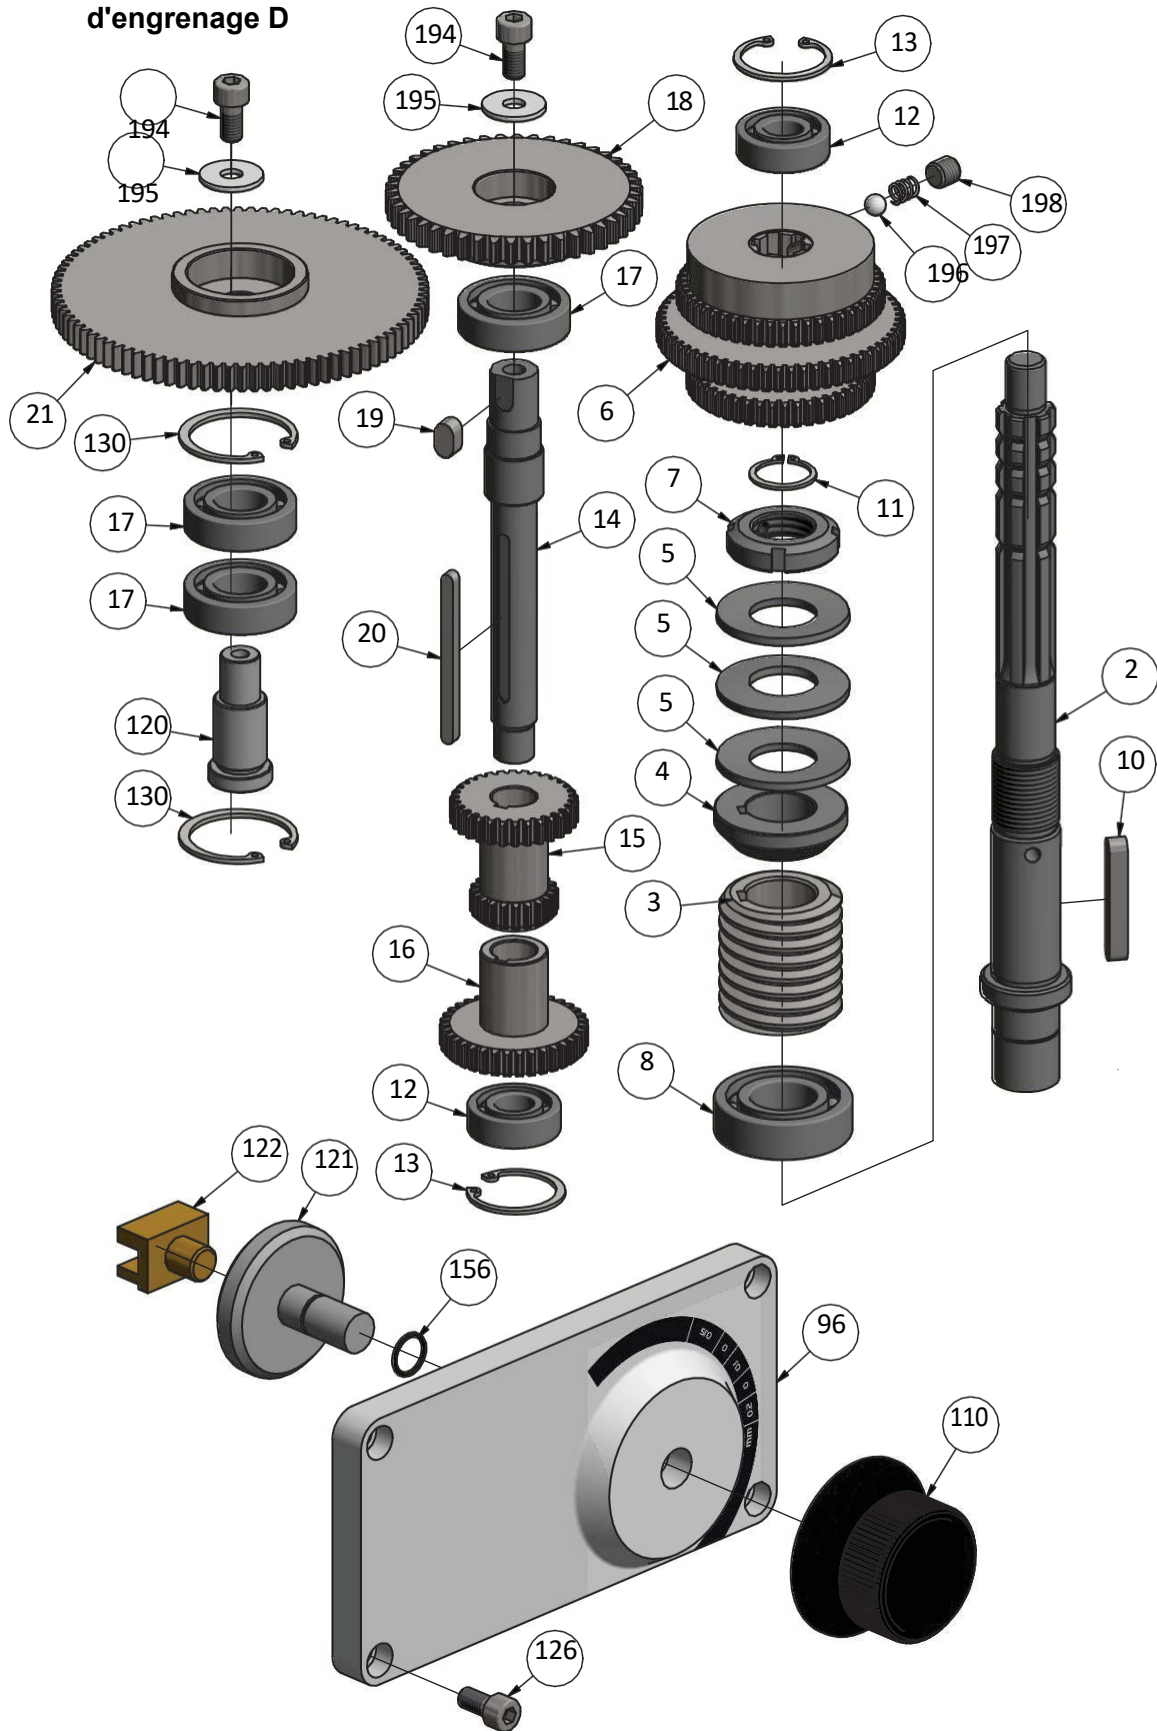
Getriebe Teil D - Section de l'engrenage D
